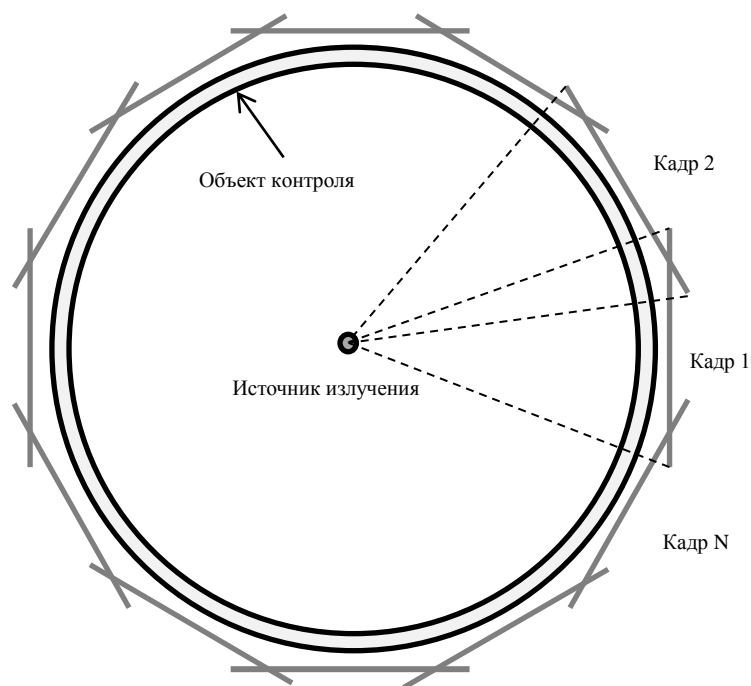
Схема радиографического контроля сварного шва
